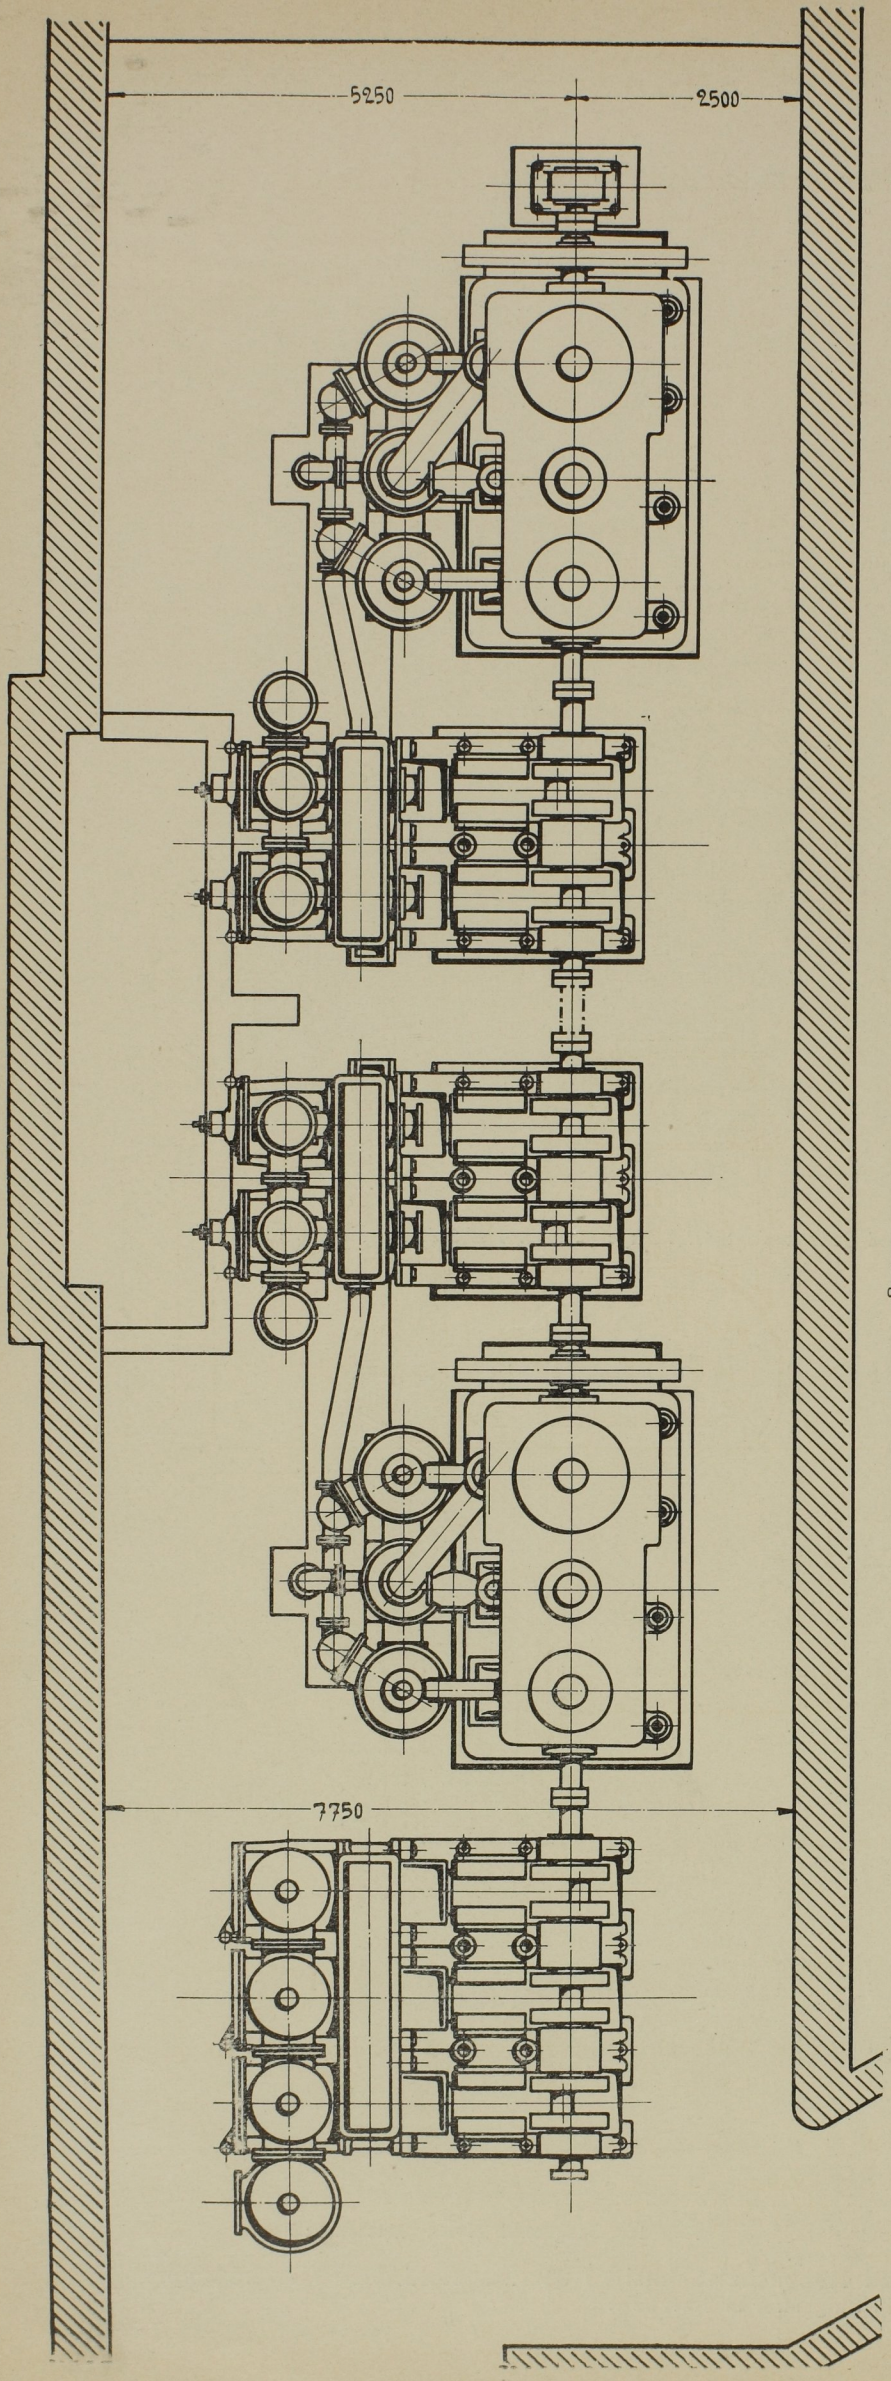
Grundriss der Maschinenanlage. Massst. 1:80.
